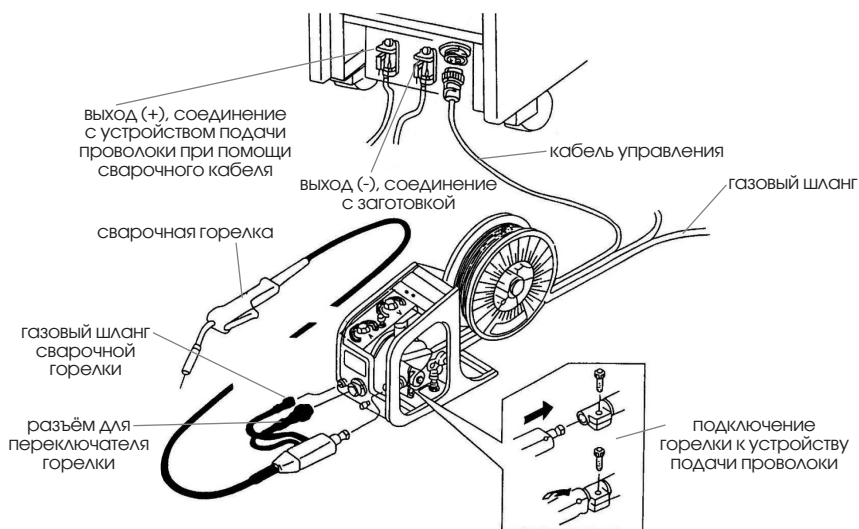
Подключение горелки, устройства подачи проволоки, сварочного кабеля и кабеля управления.
